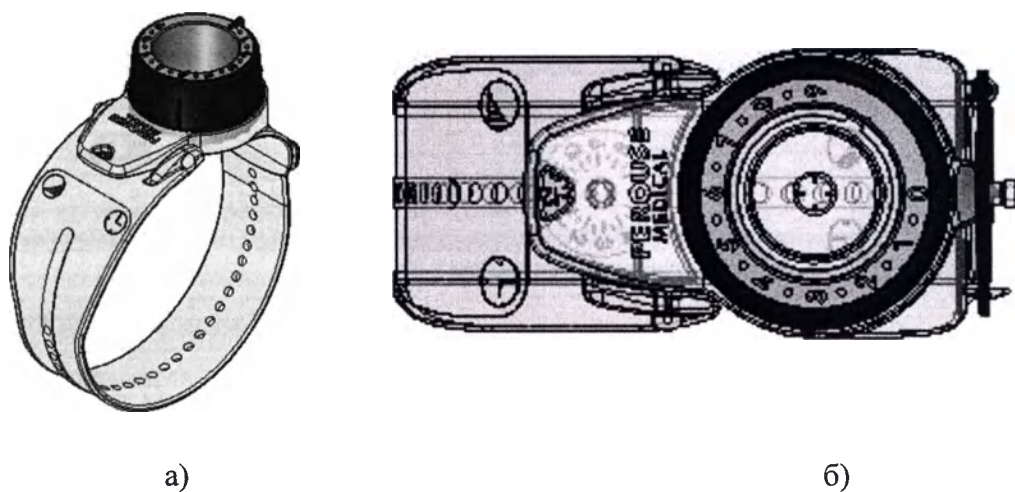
Изображение Seal One: а) вид сбоку; б) вид сверху
